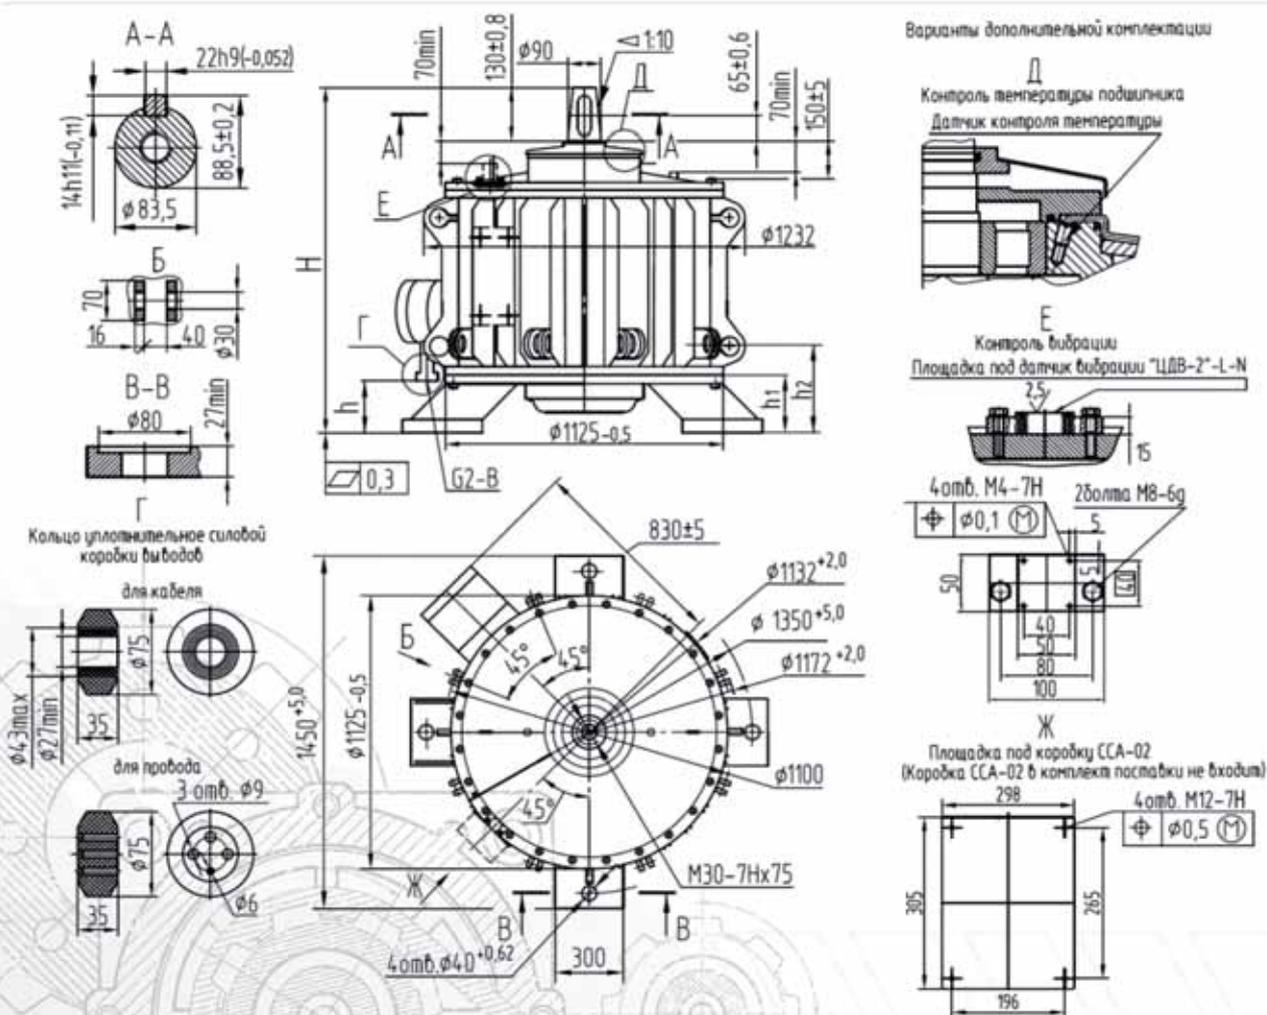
Габаритные и присоединительные размеры двигателей ВАСО5К
